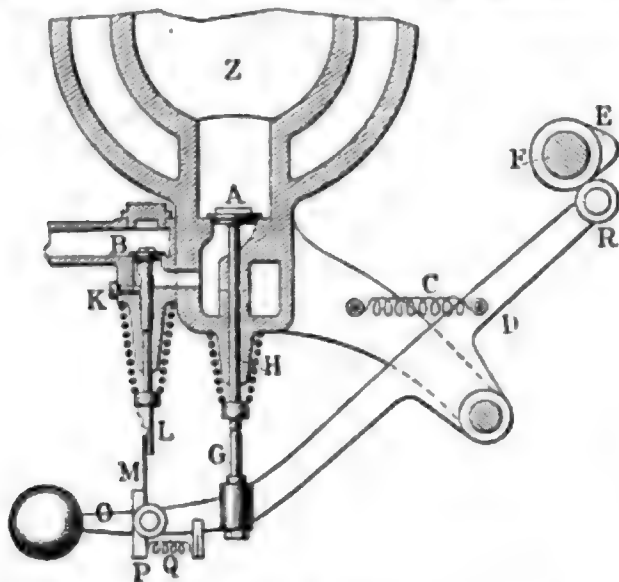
Regulator für Gaskraftmaschinen von Crofley u. Komp.
